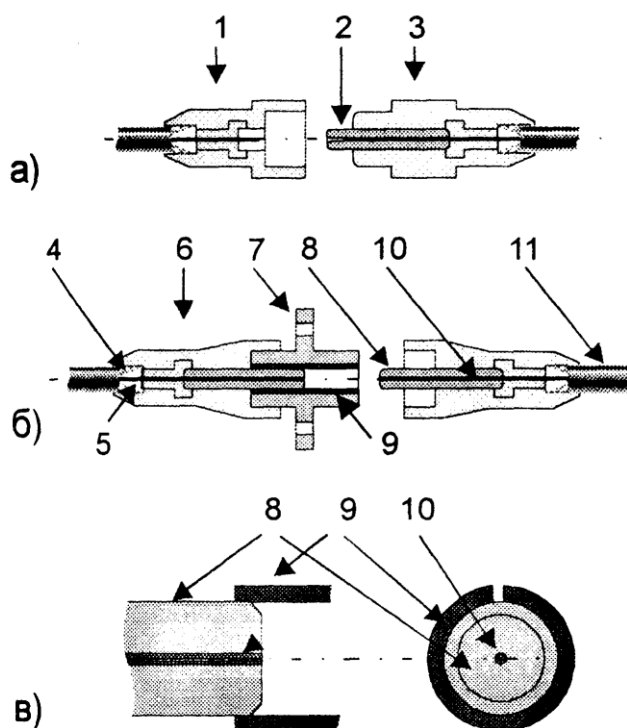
Конструкции соединителей: а) – несимметричная, б) – симметричная, в) – наконечник и центратор розетки симметричного соединителя: 1 – соединитель гнездовой; 2 – наконечник-капилляр; 3 – соединитель штекерный; 4 – кевларовые нити; 5 – эпоксидный наполнитель; 6 – соединитель; 7 – переходная соединительная розетка (адаптер); 8 – оптический наконечник; 9 – центрирующий элемент розетки; 10 – оптическое волокно; 11 – миникабель
